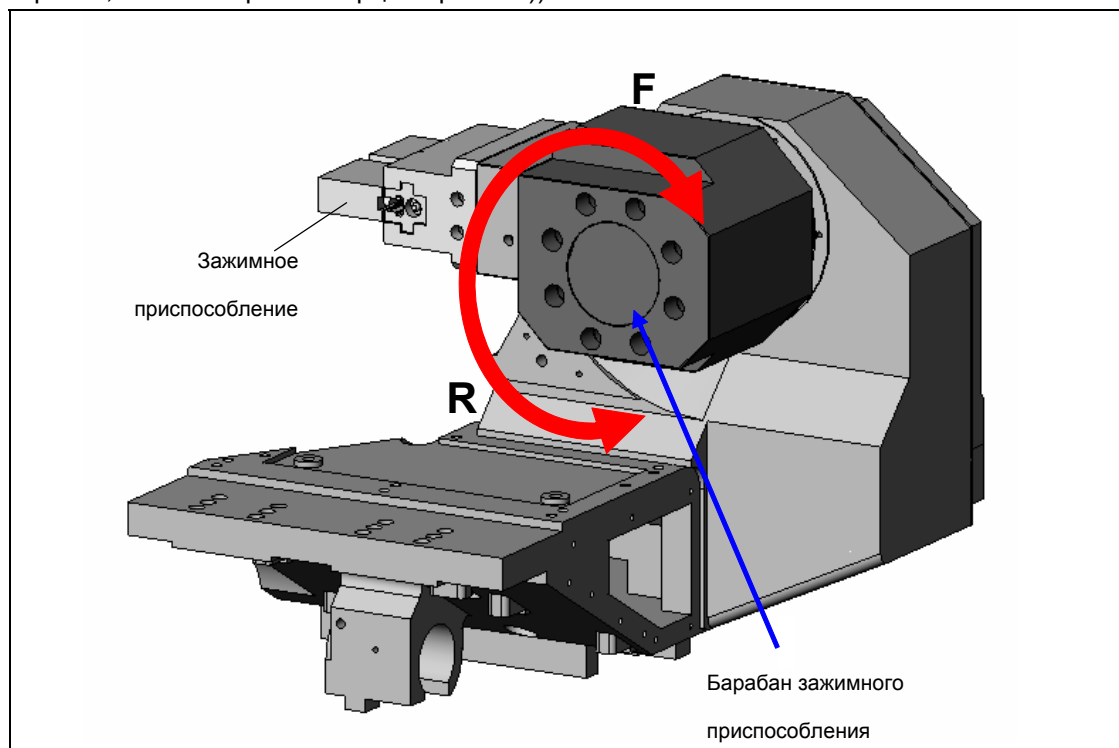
Устройство загрузки-разгрузки заготовки
